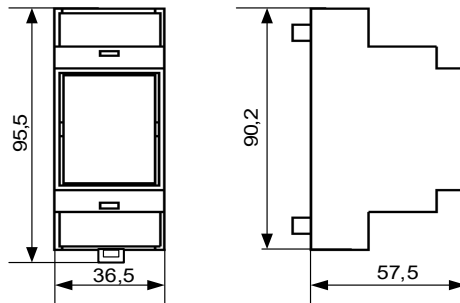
Габаритные и присоединительные размеры преобразователя
